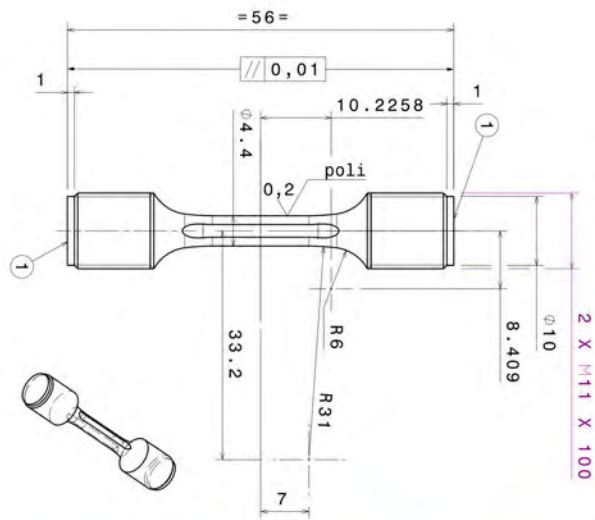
Géométrie des éprouvettes d'intrusion-extrusion.
